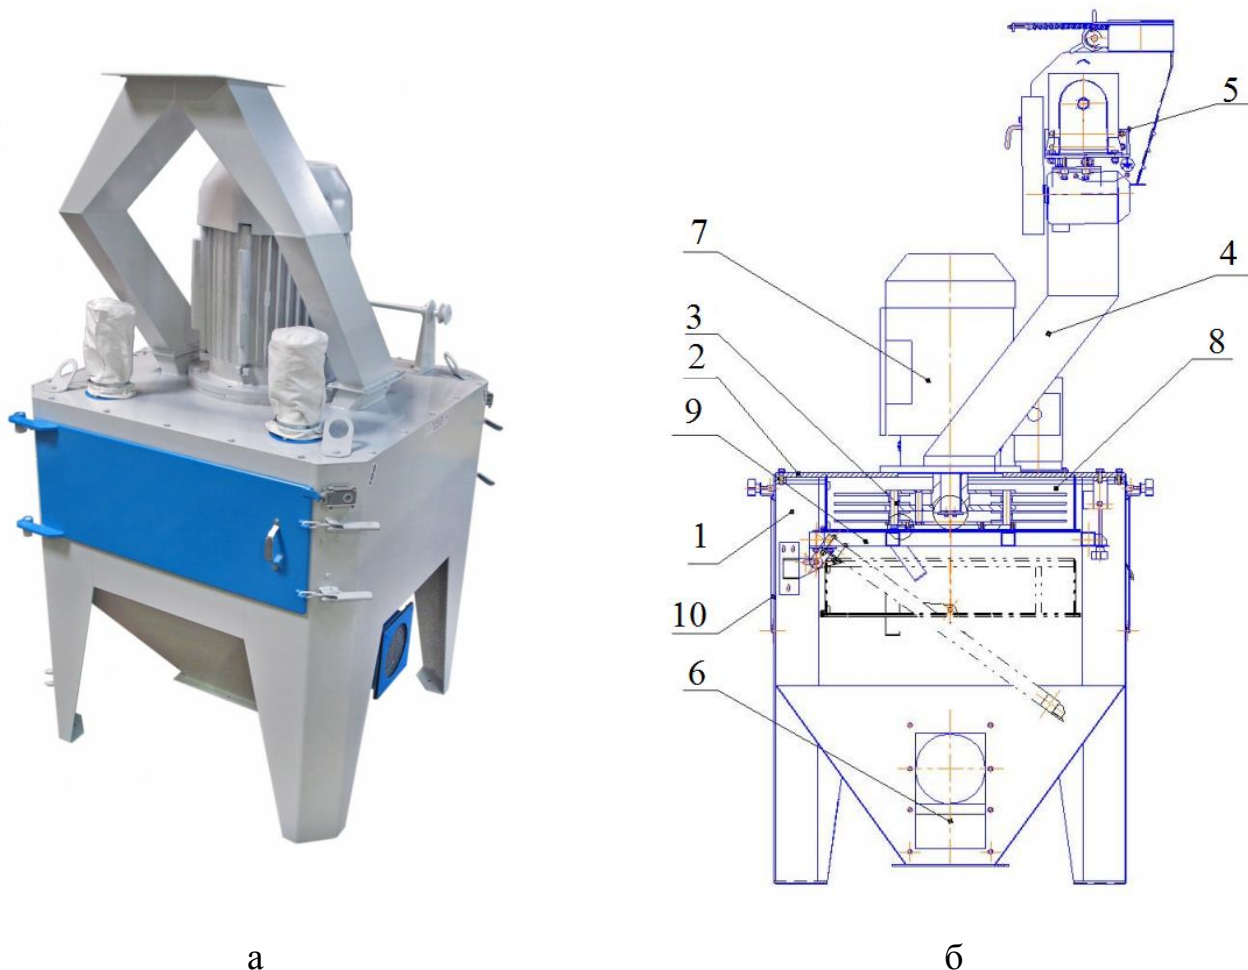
Дробарка молоткова А1-ДМ2Р-В (Україна): а – загальний вигляд; б – конструкційна схема: 1 – станина; 2 – кришка для ротора; 3 – ротор із молотками; 4 – приймач; 5 – живильний патрубок; 6 – захисна камера; 7 – електро двигун; 8 – корпус для встановлення сита; 9 – кріплення корпуса сита; 10 – оглядова дверцята. [10]
